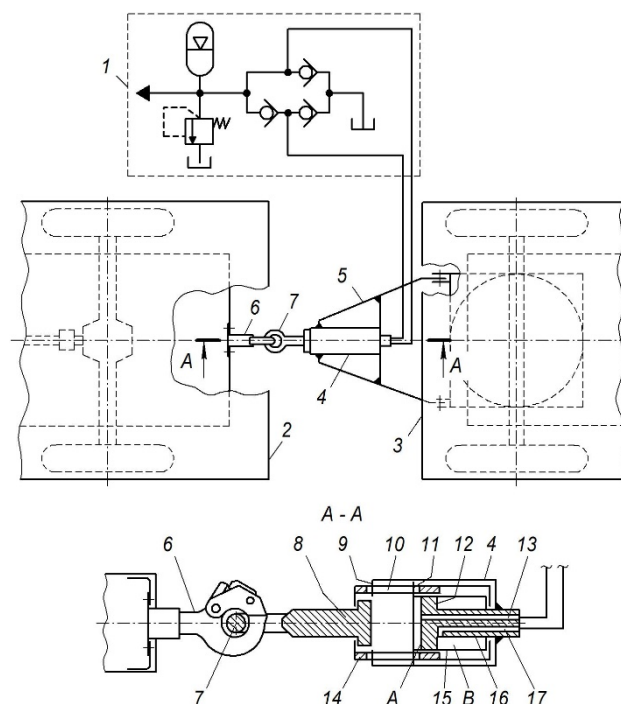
Схема пневмогидравлического сцепного устройства с демферным и амортизационным механизмами: *A, B* – поршневая и штоковая полости; *1* – рекуперативный гидропривод; *2* – лесовозный автомобиль; *3* – прицеп; *4* – корпус; *5* – дышло; *6* – крюк; *7* – присоединительная петля; *8* – фланец; *9, 11* – ограничители; *10* – сквозные пазы; *12* – поршень; *13, 17* – каналы; *14* – ограничитель подвижного цилиндра; *15* – гидроцилиндр двухстороннего действия; *16* – шток
